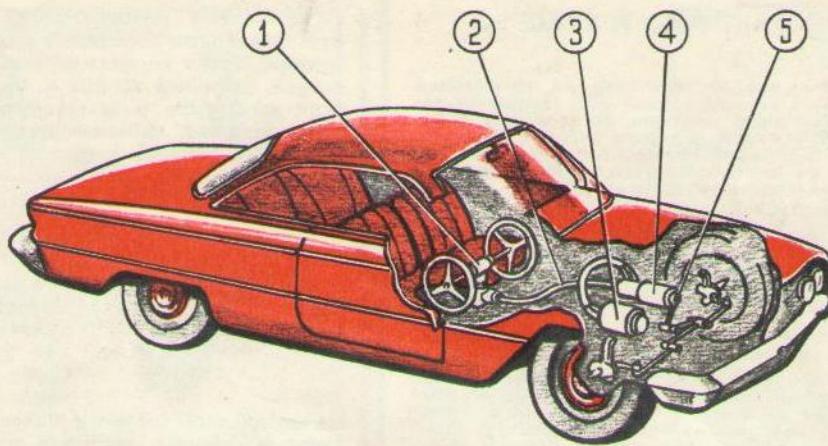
Система Матеу Ваканте: 1 — червячная передача; 2 — гибкий вал; 3 — рулевой механизм; 4 — насос усилителя; 5 — рулевой привод.
